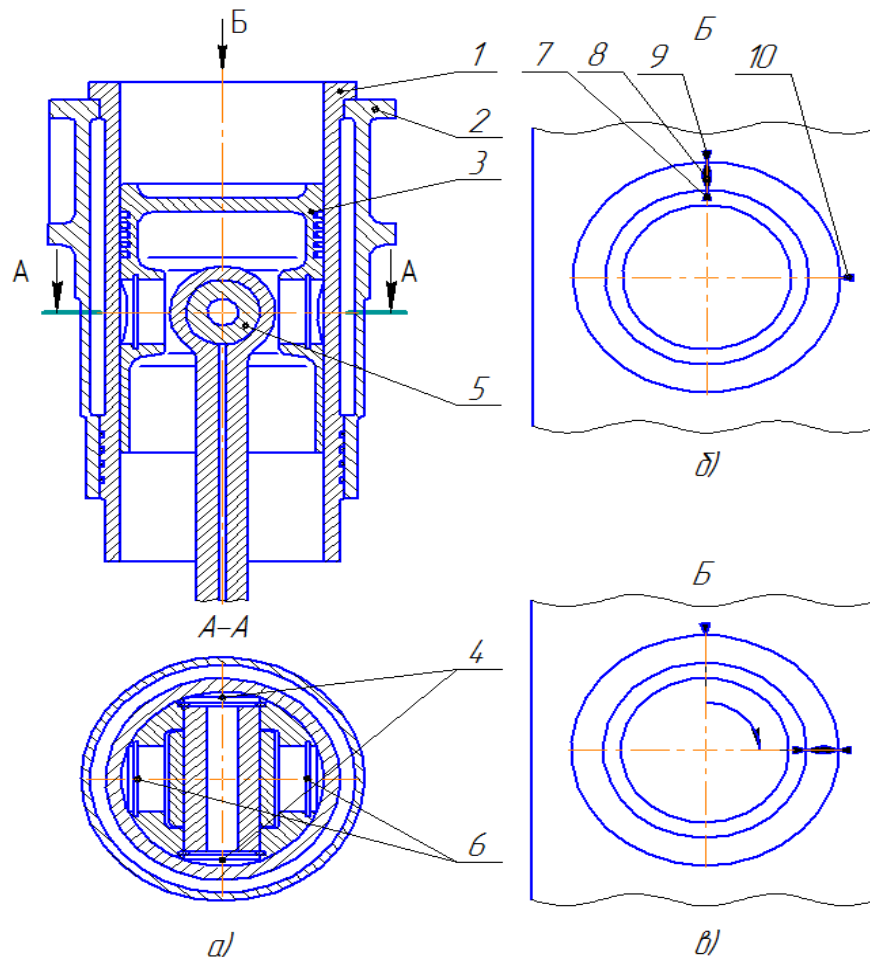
Циліндро-поршнева група тронкового двигуна:
